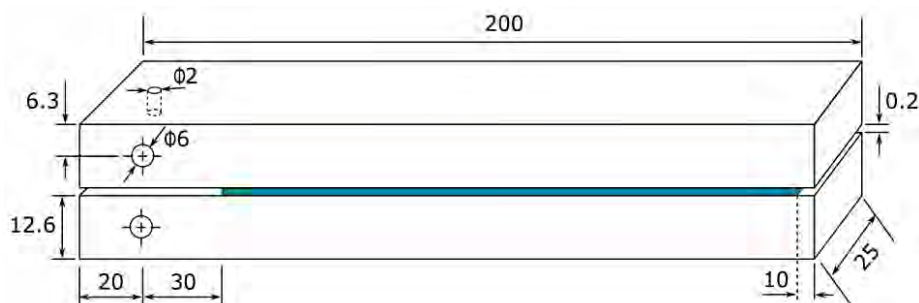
Dimensions (en mm) des éprouvettes DCB pour les essais en mode I (selon la norme (BS 7991, 2001)).
